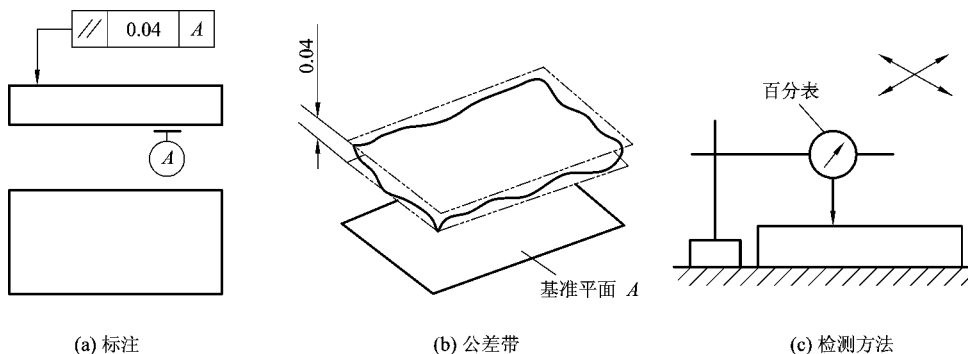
平行度的标注、公差带及检测方法
